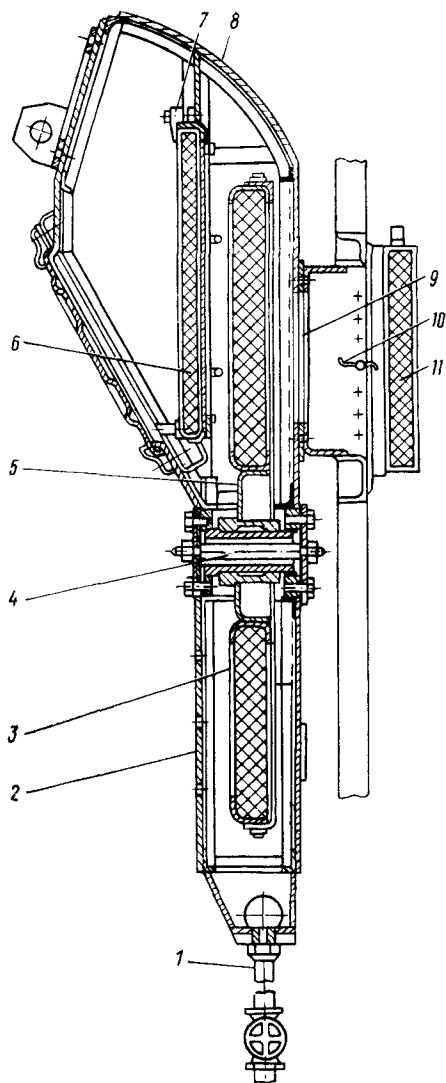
Унифицированный воздухоочиститель непрерывного действия:
